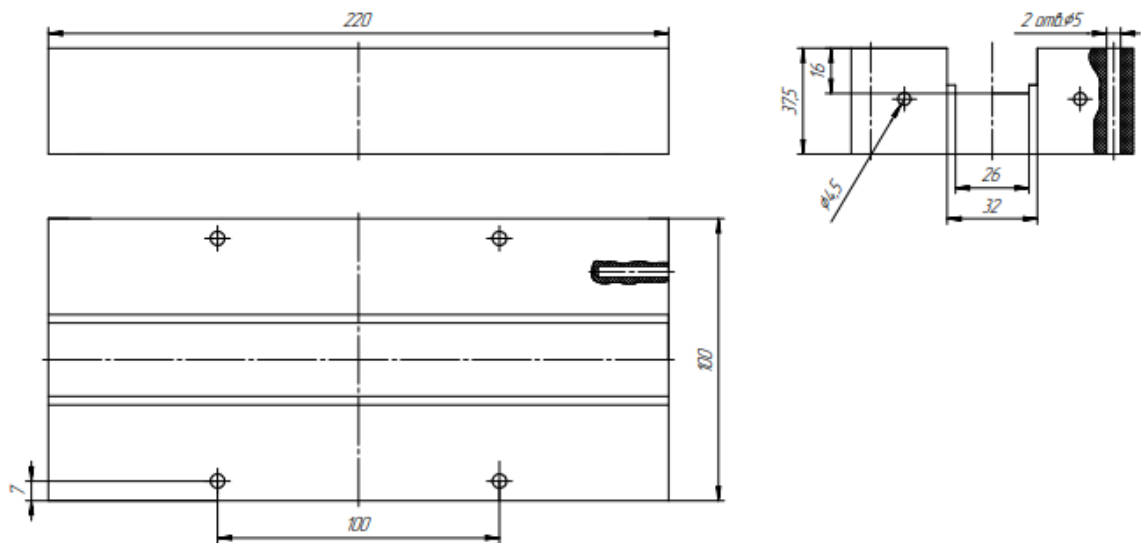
Кондуктор для зварювання фланцем до дослідного зразку.
